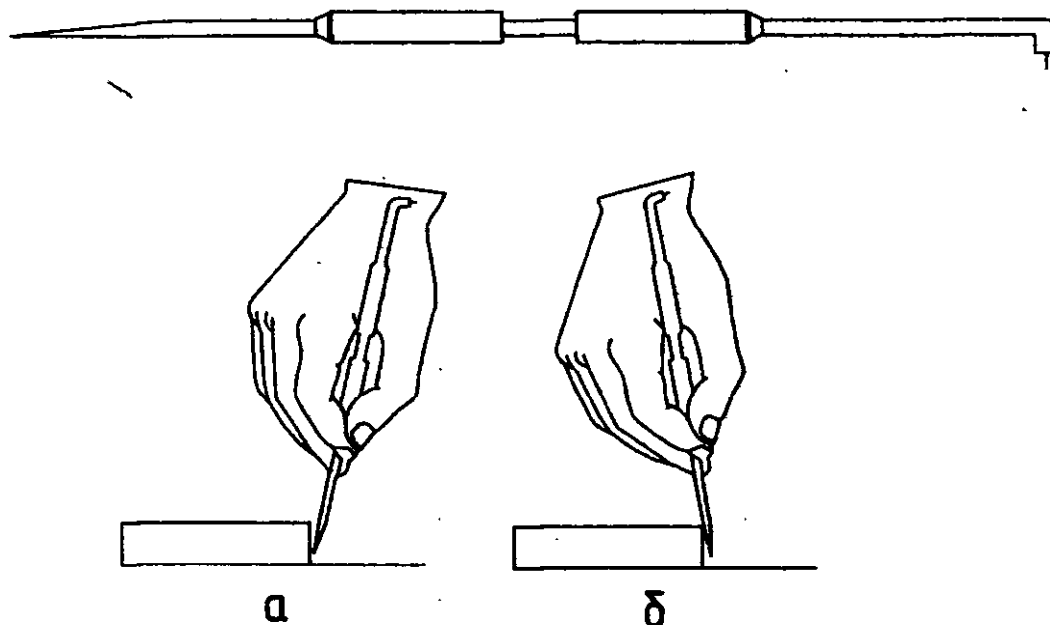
Правильный (а) и неправильный (б) приемы нанесения чертилкой разметочных рисок.
